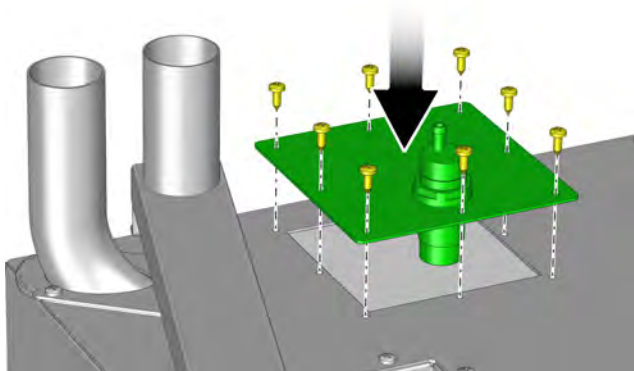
Plaque de montage du capteur de niveau de remplissage
